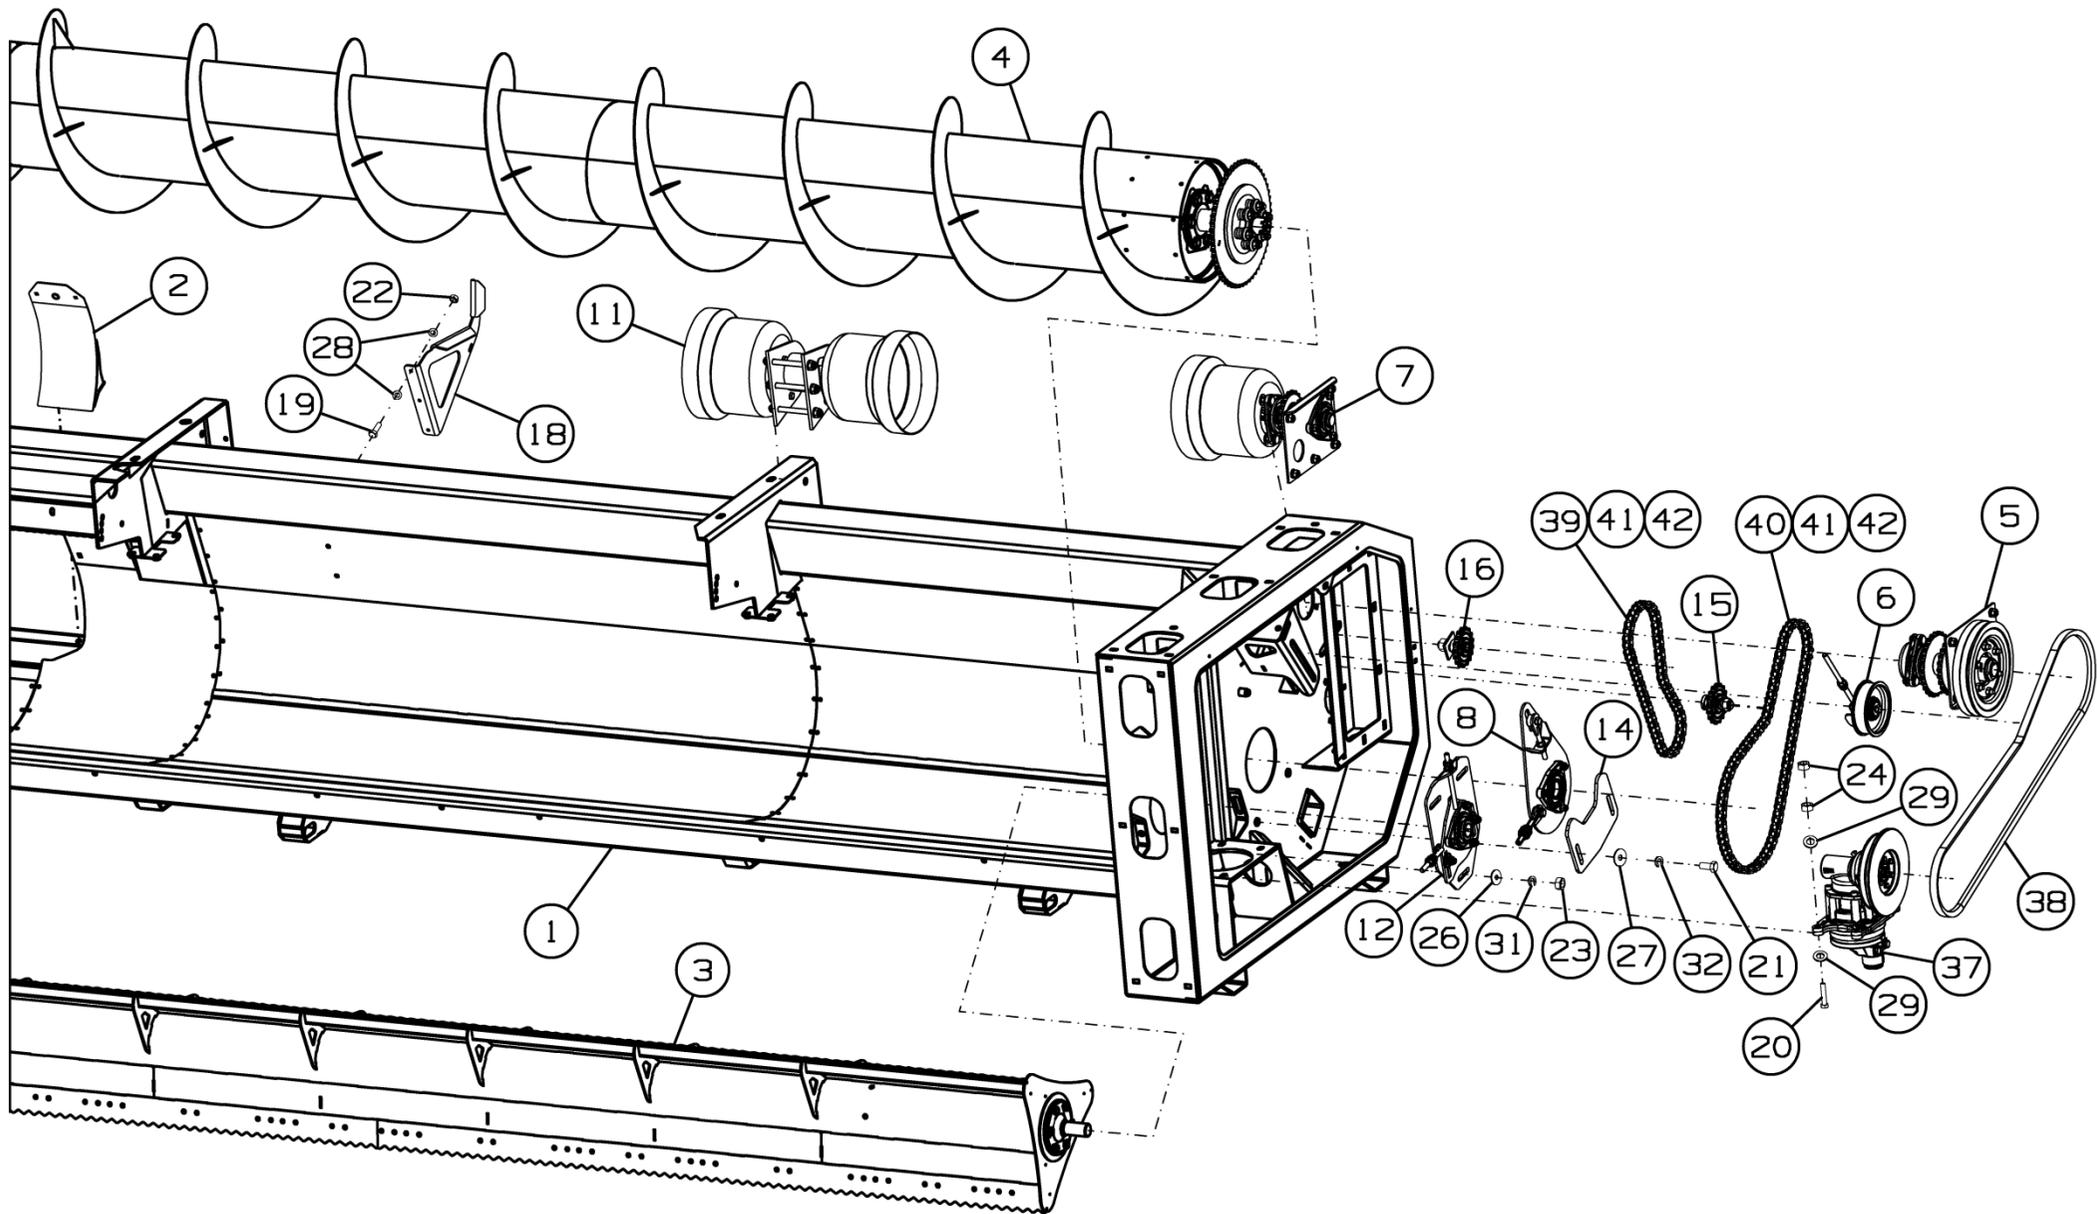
Корпус жатки SS-780.01.01.000У-01
